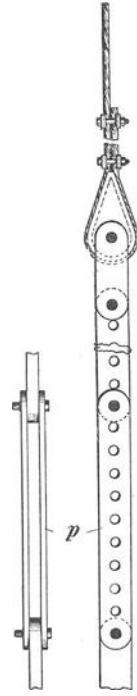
Laschenverbindung zum Ausgleich der Seillängen.
